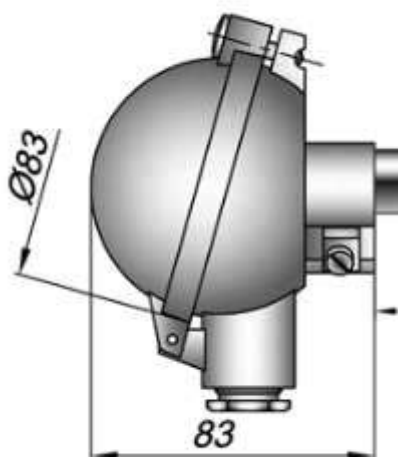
Габаритные размеры алюминиевой головки с защелкой
